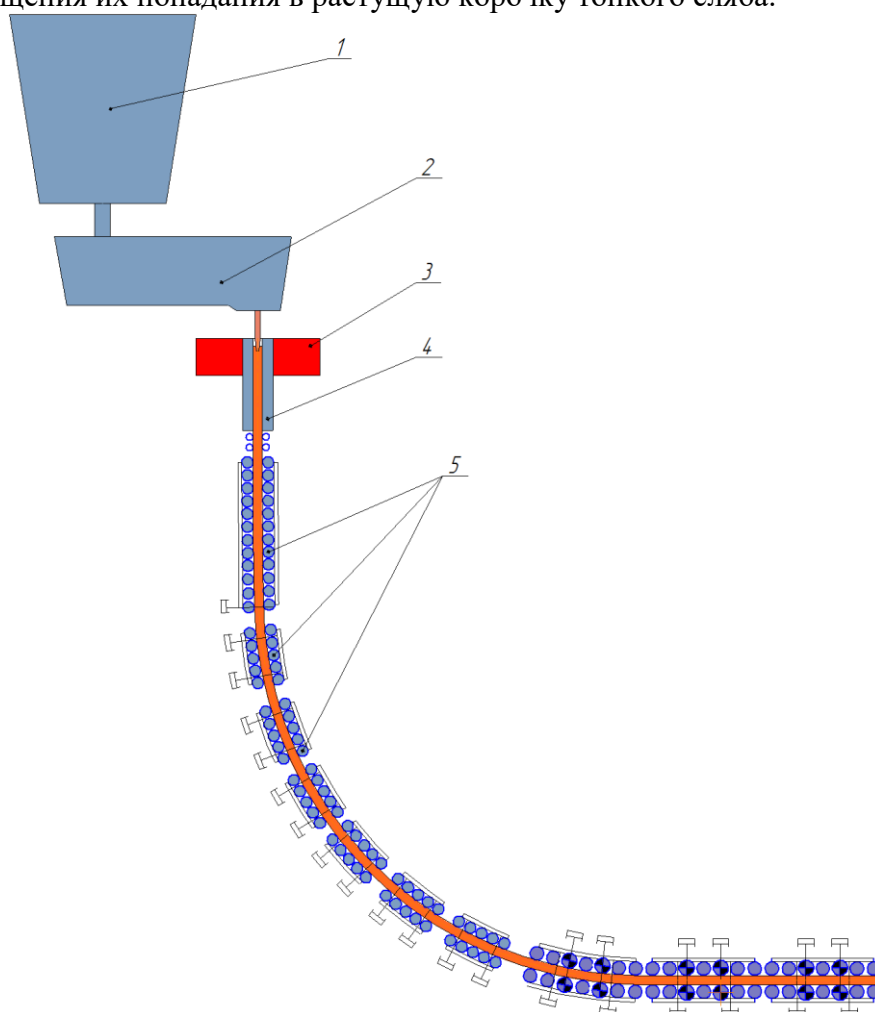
Схема машины непрерывной разливки стали: 1 – сталеразливочный ковш; 2 – промежуточный ковш; 3 – электромагнитный тормоз; 4 – кристаллизатор; 5 – сегменты роликовой проводки.
